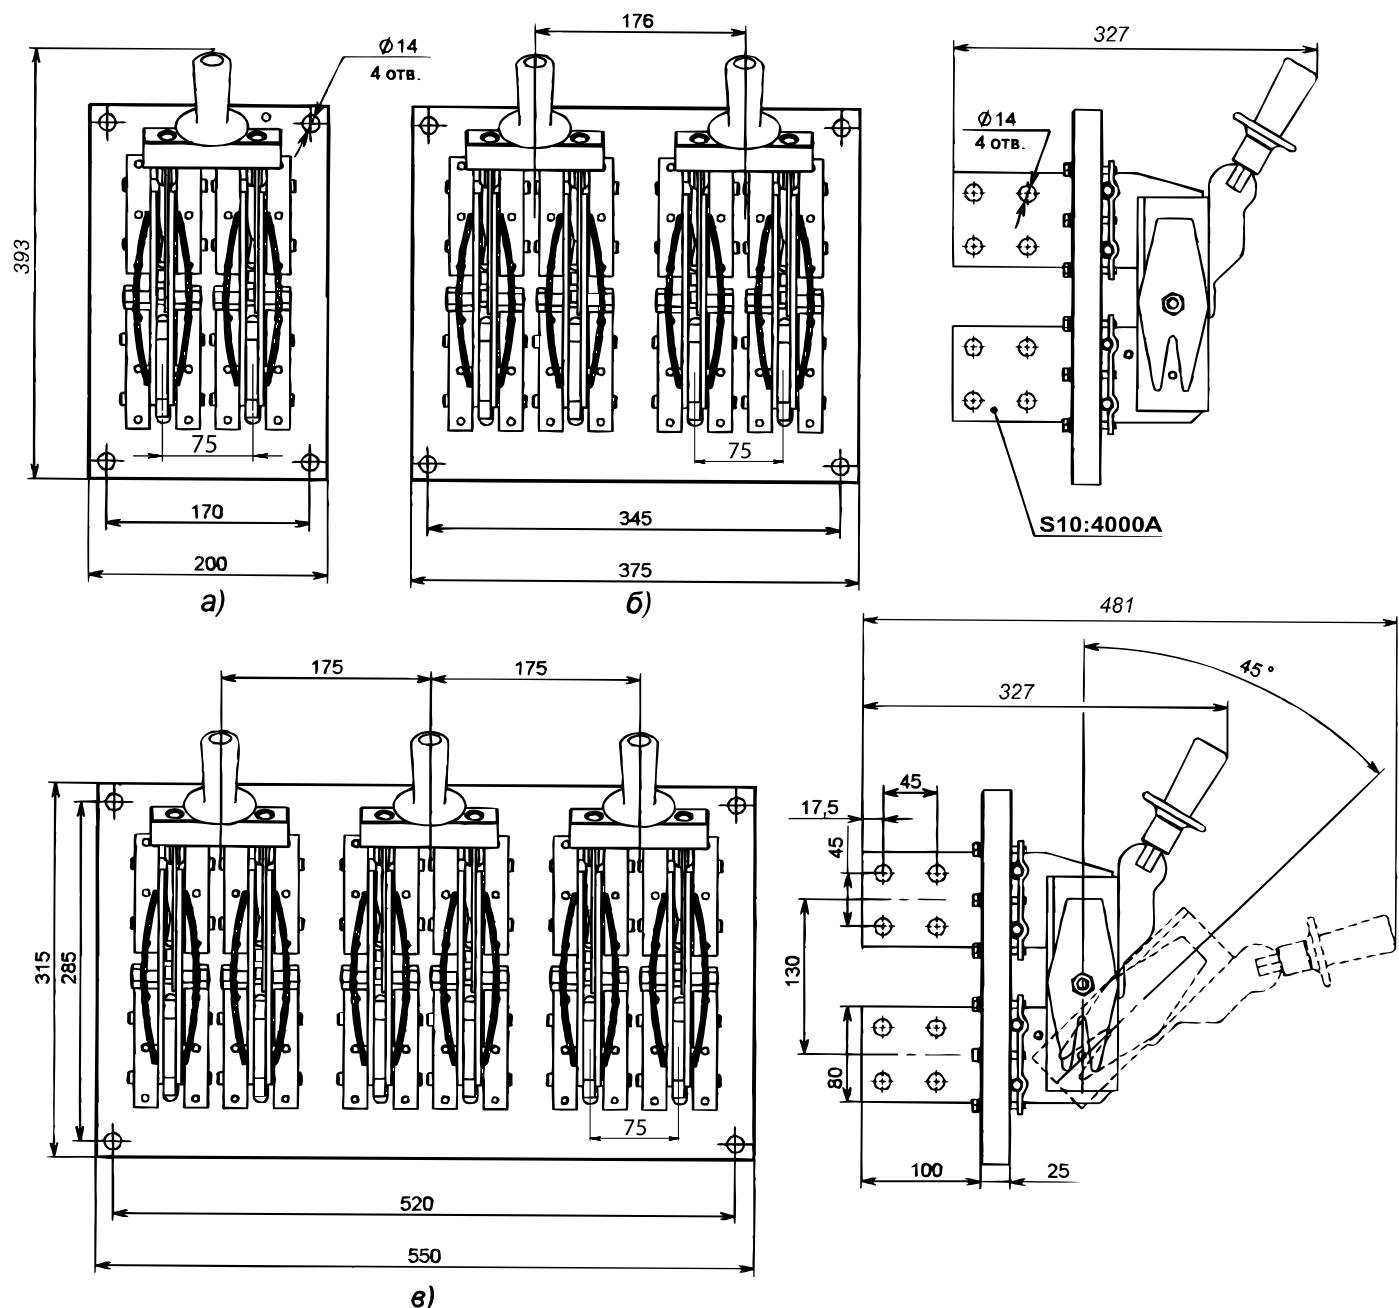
Разъединитель РЕ19 с центральным рычагом для управления штангой
